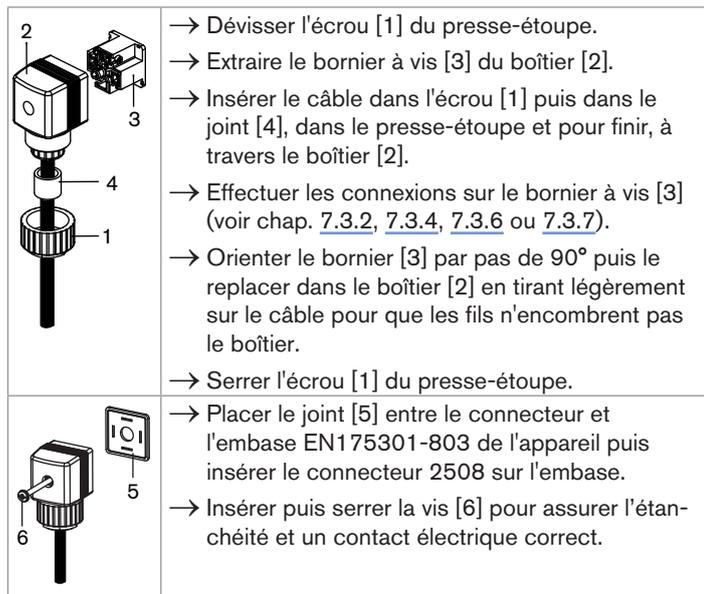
Assemblage du connecteur femelle type 2508 (fourni)
